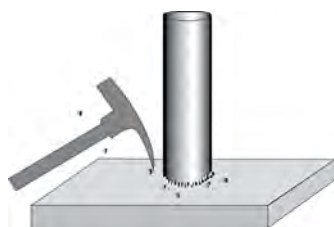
Desconchado de residuos de flujo de soldadura
